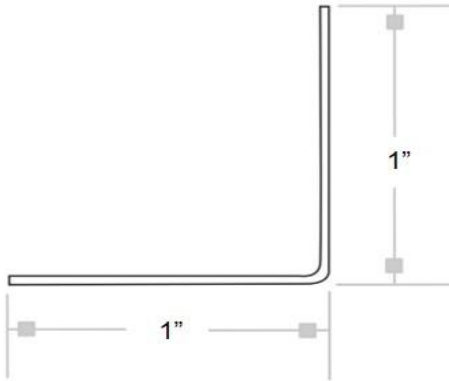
Sección transversal de ángulo (REY, 2016)
